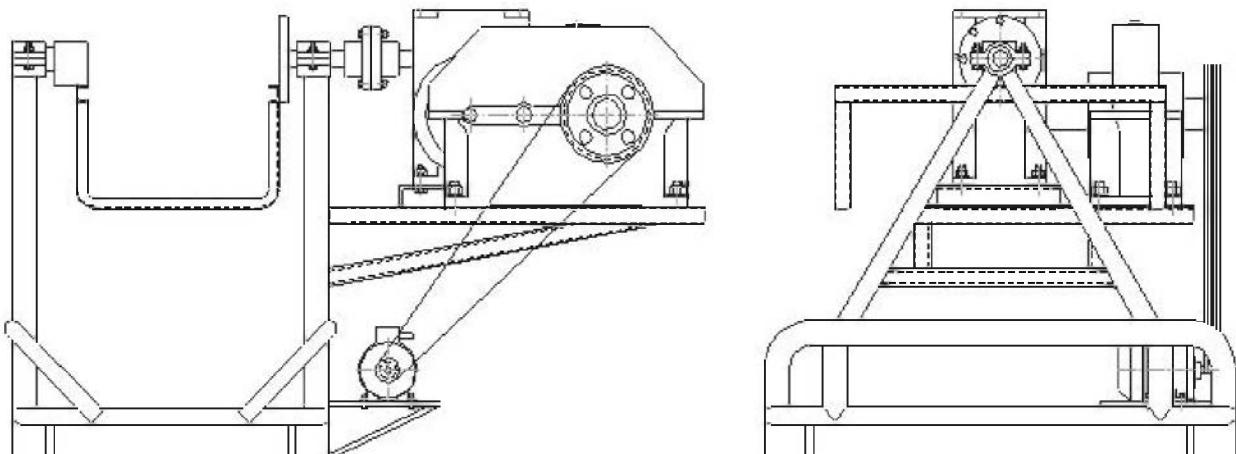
Стенд для разборки – сборки двигателя
